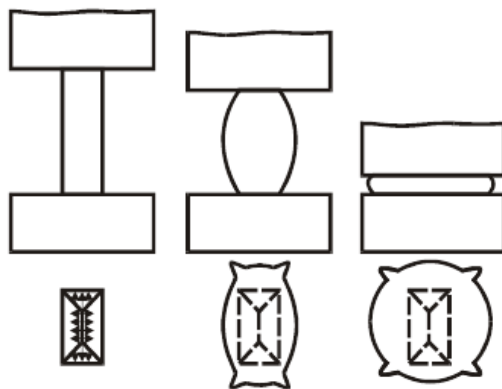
Схема движения частиц металла при осадке заготовки прямоугольного сечения
